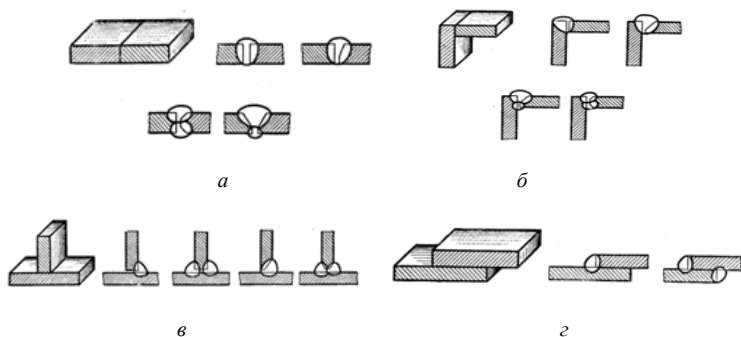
Виды сварных соединений: *a* – стыковые; *б* – угловые; *в* – тавровые; *г* – нахлесточные
